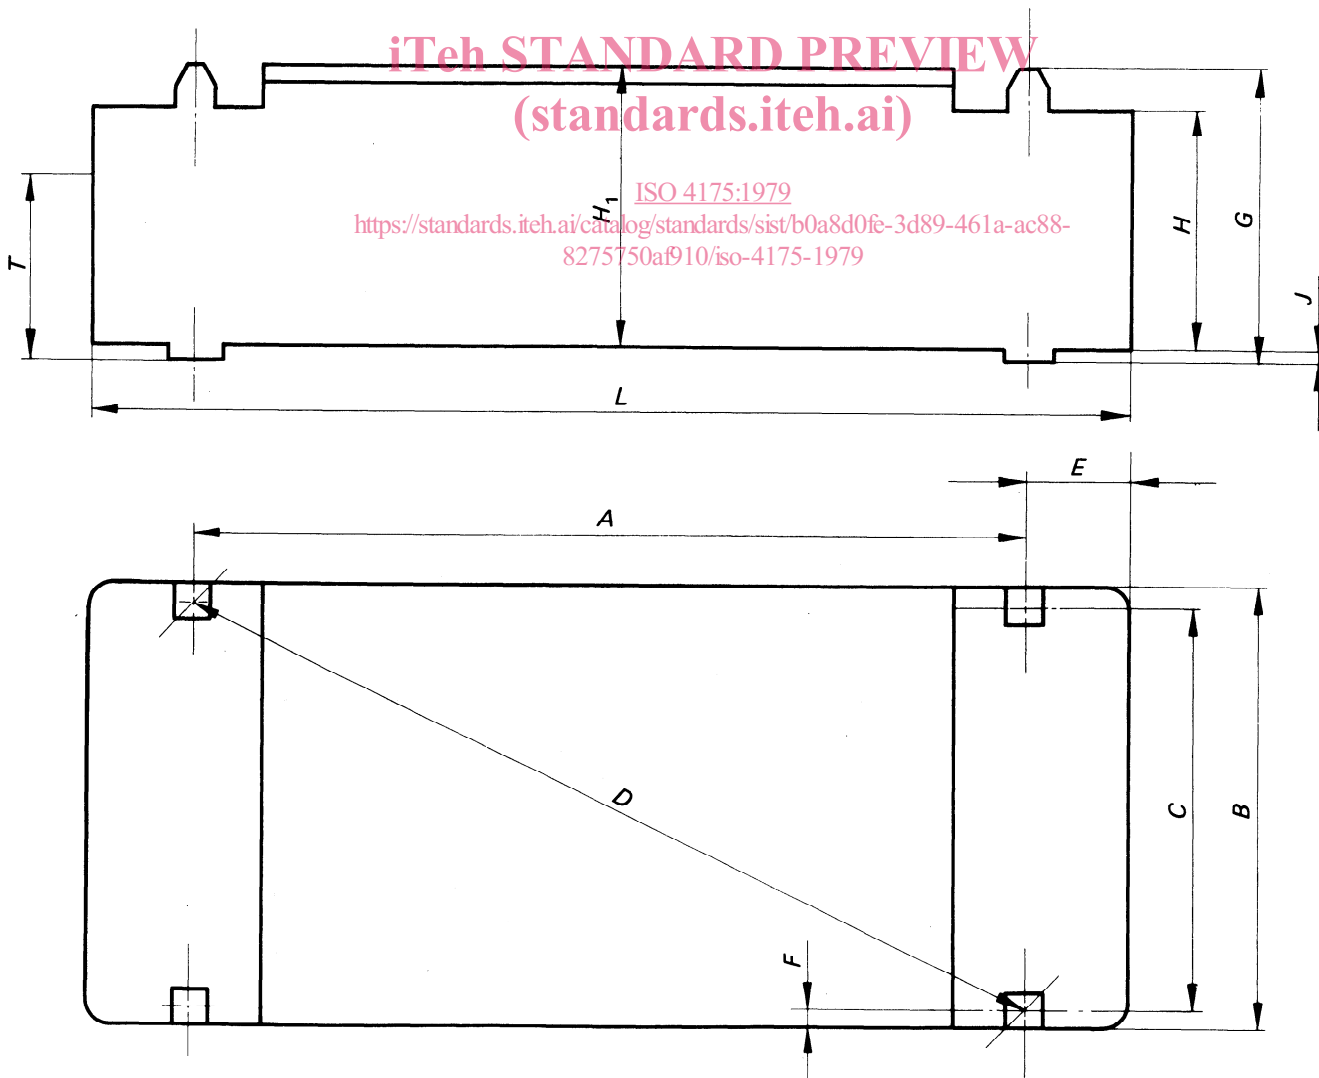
Principales dimensions, et dimensions des principaux éléments de construction
